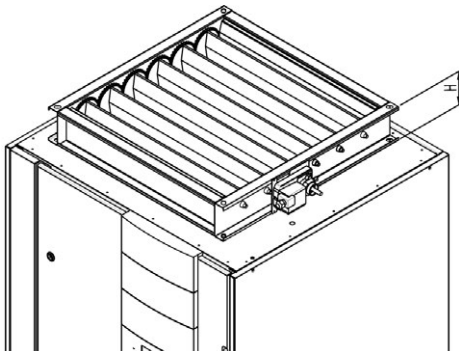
Draufsicht EC Tower ECD 502 mit Adapterblech
